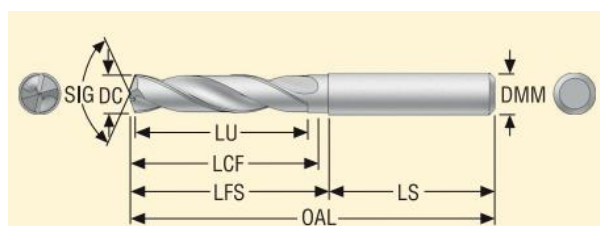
Свердло SD1103-0900-035-10R1 [2, с. 28]
